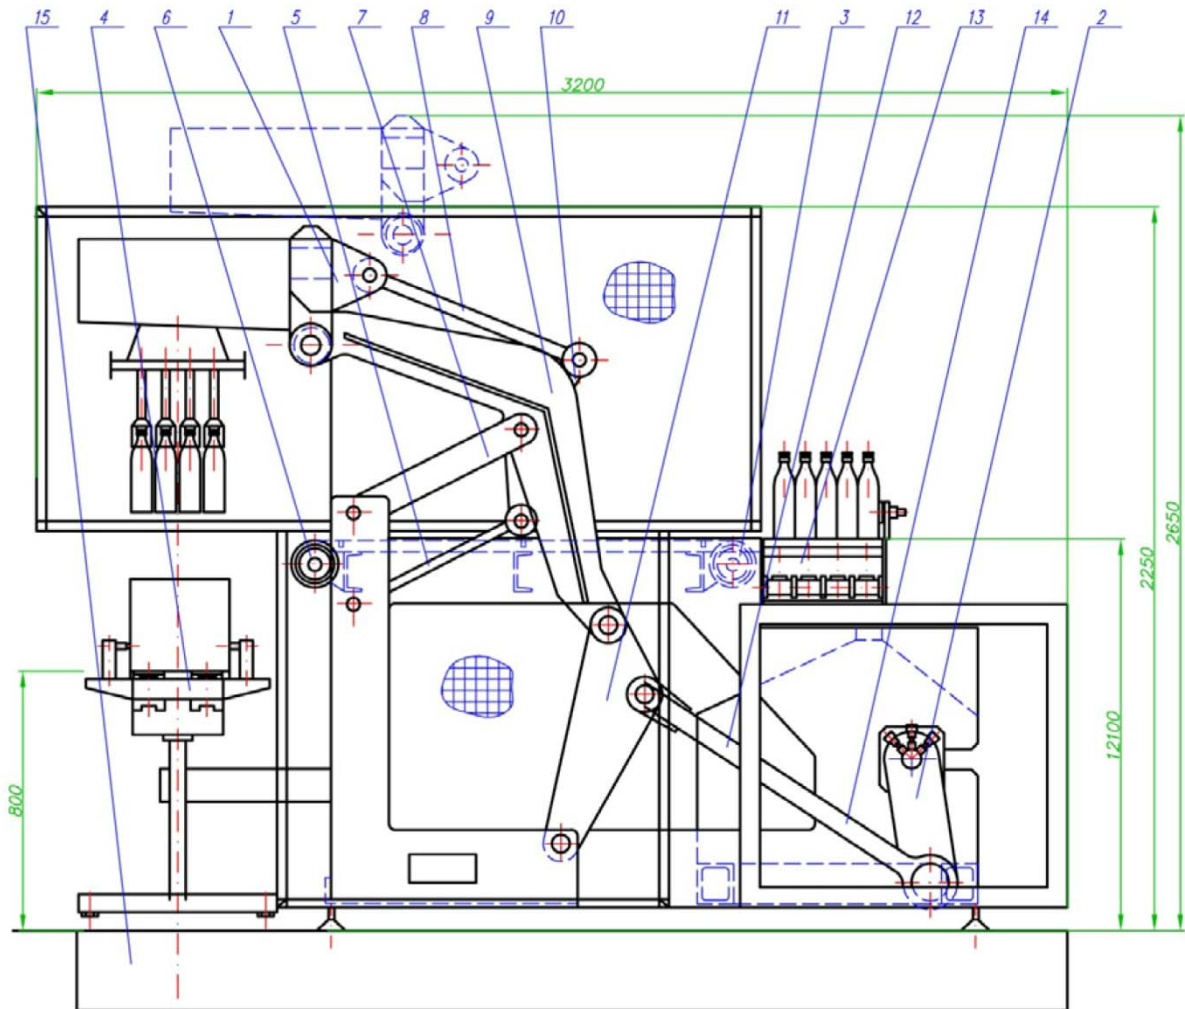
Загальний вигляд механічного розвантажувача пляшок марки VL 2: 1 – голова; 2 – привід; 3 - ведучій вал; 4 - конвеєр ящиків; 5 – цапфа; 6 - ведений вал; 7 – балансир; 8 – тяга; 9 – плече; 10 – важіль; 11 – дворамено; 12 - станина; 13 - конвеєр пляшок; 14 – шатун; 15 - фундамент
